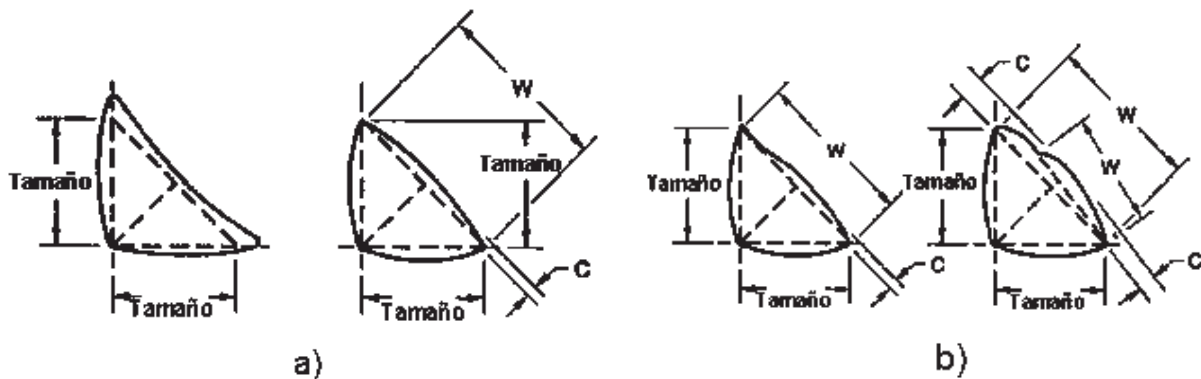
Perfiles de soldaduras de filete, a) Perfiles deseables y b) Perfiles aceptables.
